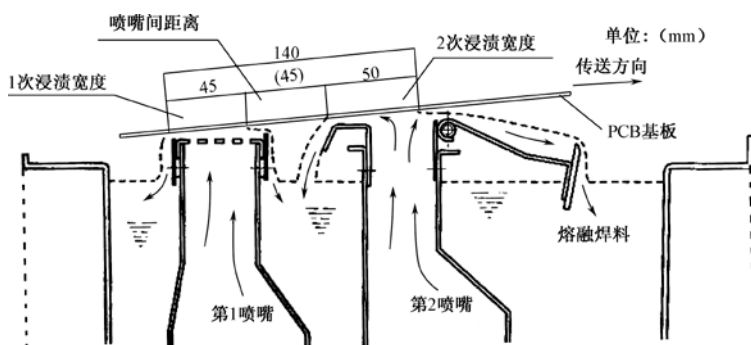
无铅波峰焊接设备喷嘴布局
